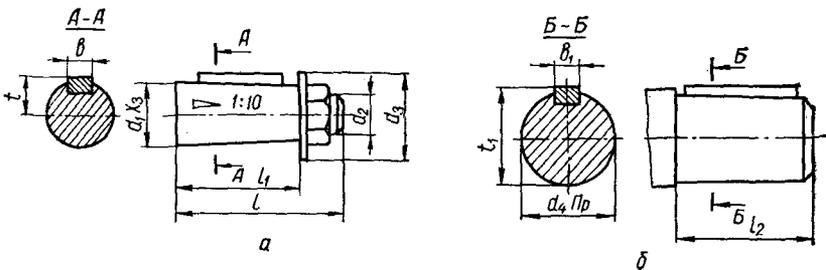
Присоединительные размеры концов валов редукторов РЦД:
